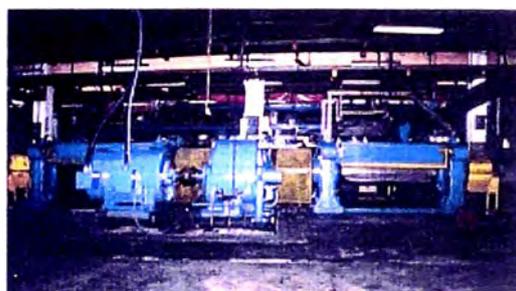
ELEVACION DE EXTRUSORA SIMPLE
